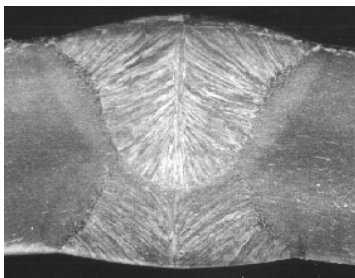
Макроструктура сварного шва, с подваркой
